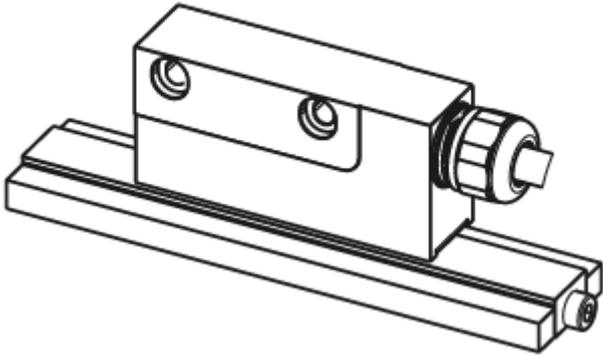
Montagebeispiel - Magnetband, stirnseitig verschraubt
